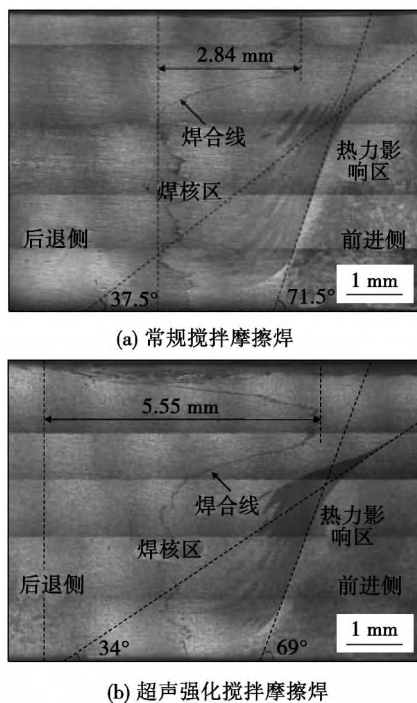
焊缝横截面纹理(600 r/min, 180 mm/min)
